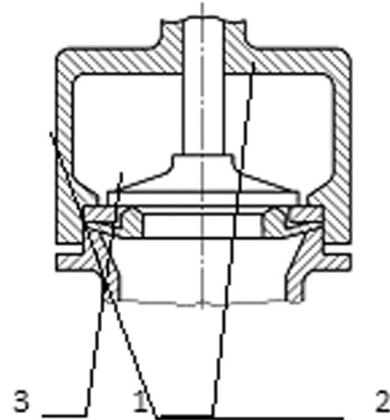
Конструкція метал-металевого затвора з демпфіруванням за допомогою пружного обмежувального кільця: 1 — золотник, 2 — сідло з обмежувальним кільцем, 3 — корпус
